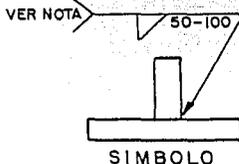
APLICACION DE SIMBOLOS DE DIMENSIONES PARA SOLDADURA DE FILETE
